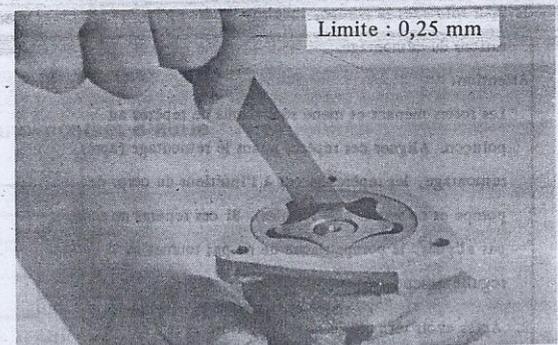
Contrôle du jeu de bout de dent de rotor
